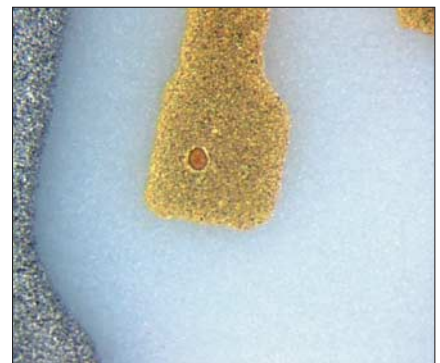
Defektes Goldpad auf einer Keramikschaltung
